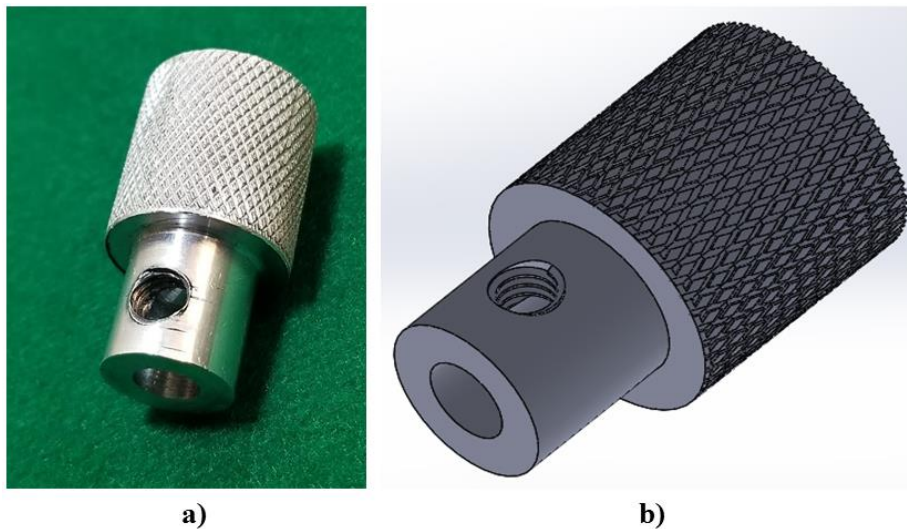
a) cabeza del tornillo maquinada, b) cabeza de tornillo diseñada.
